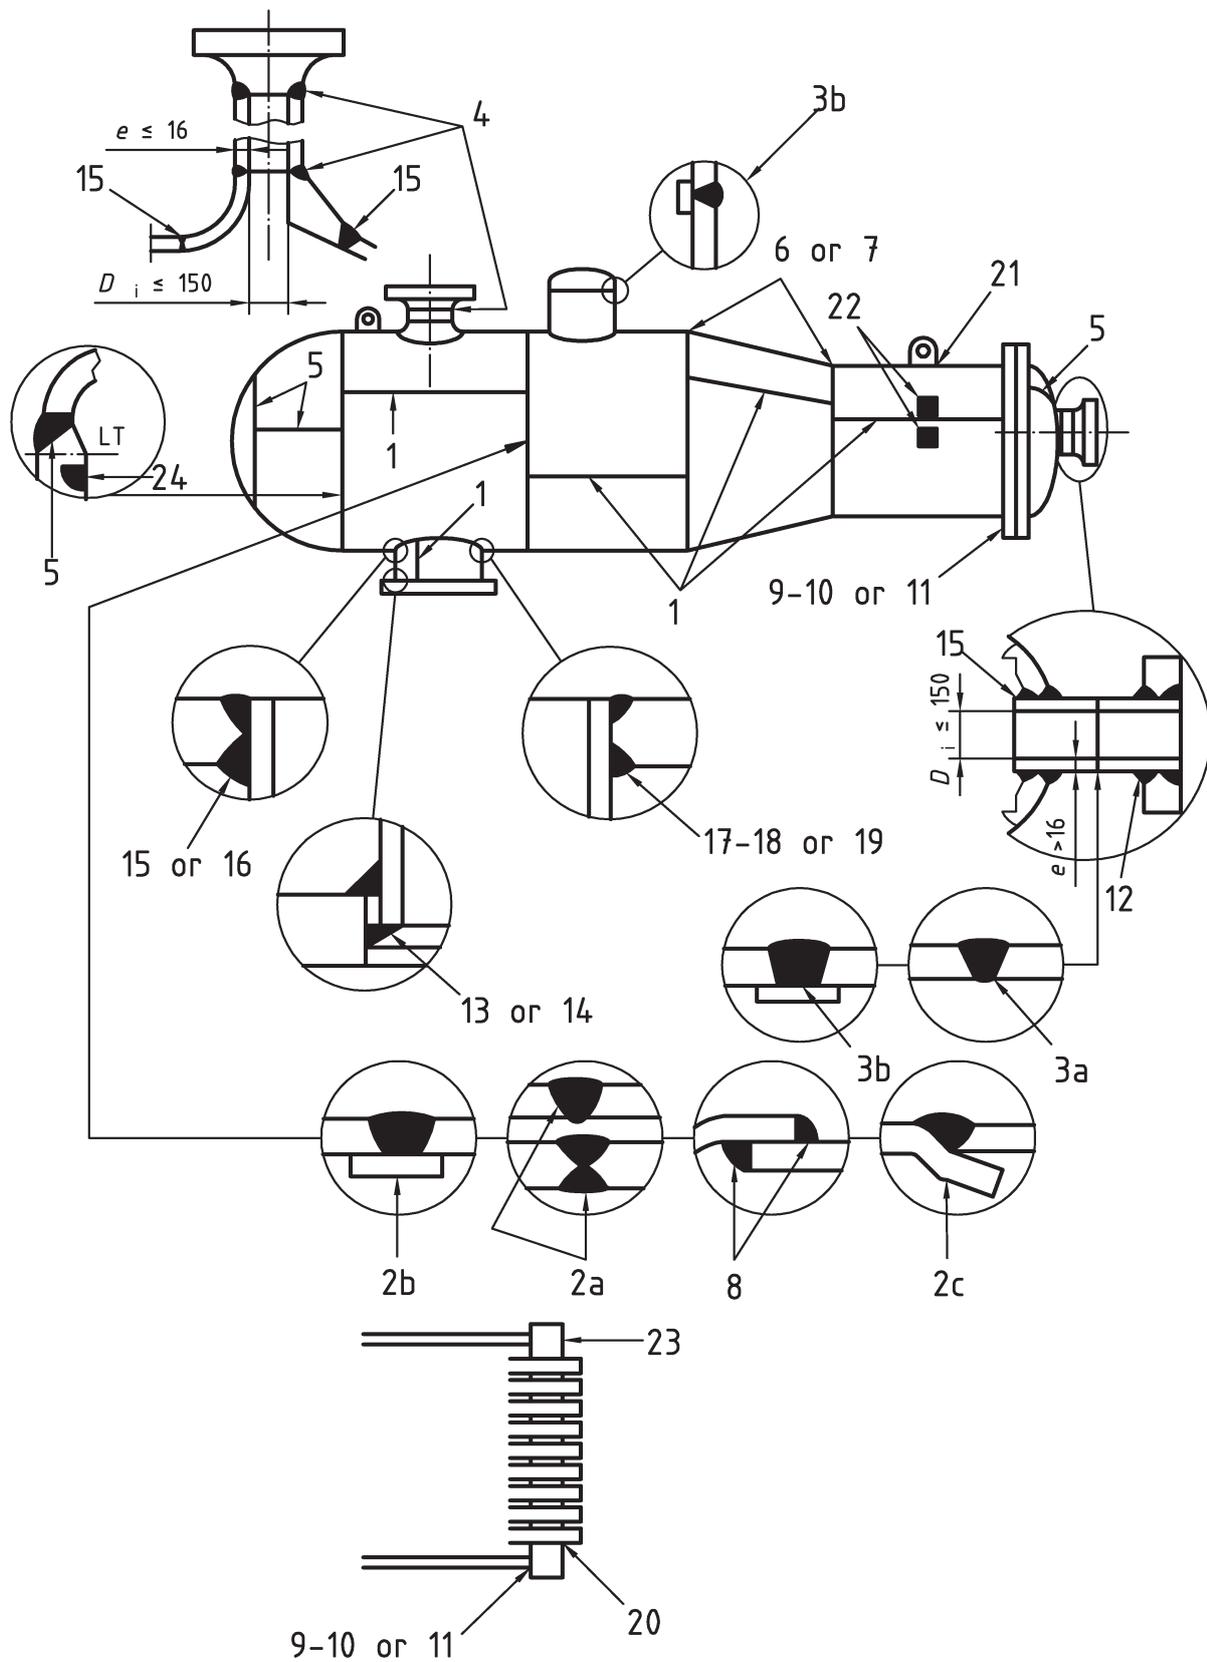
Arten von Schweißnähten
